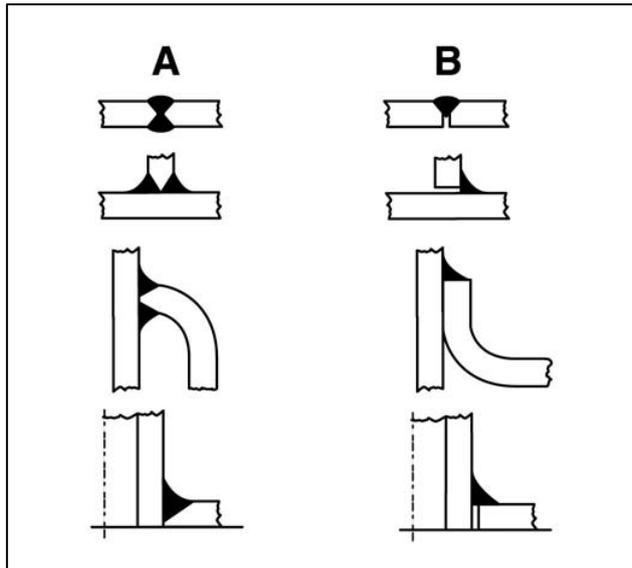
Ejemplos de realización de uniones soldadas
